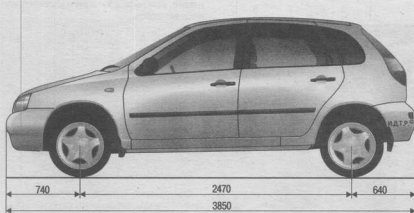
Габаритные размеры автомобиля ВАЗ-1119
